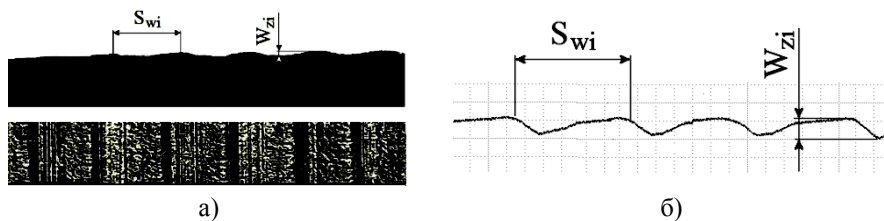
Волнистая поверхность детали после встречного концевой цилиндрической фрезерования:
